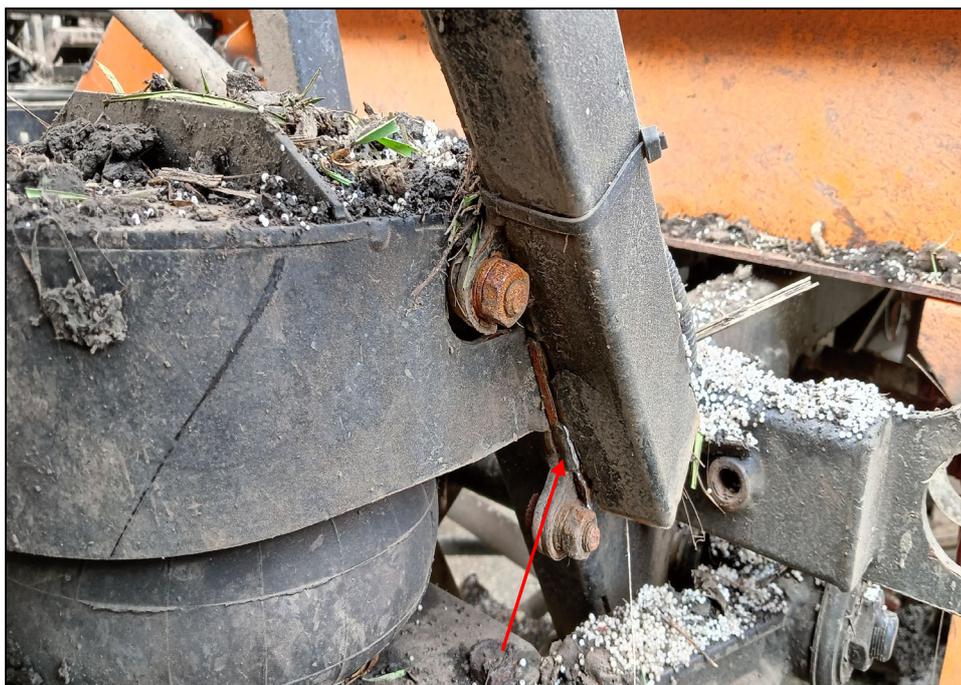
Кронштейн крепления защитного приспособления (крыла) заднего колеса
